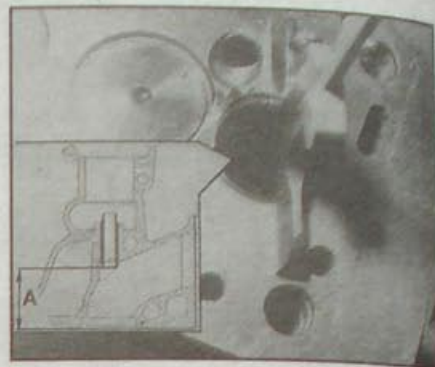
Место (А) измерения установочного размера направляющей втулки:
